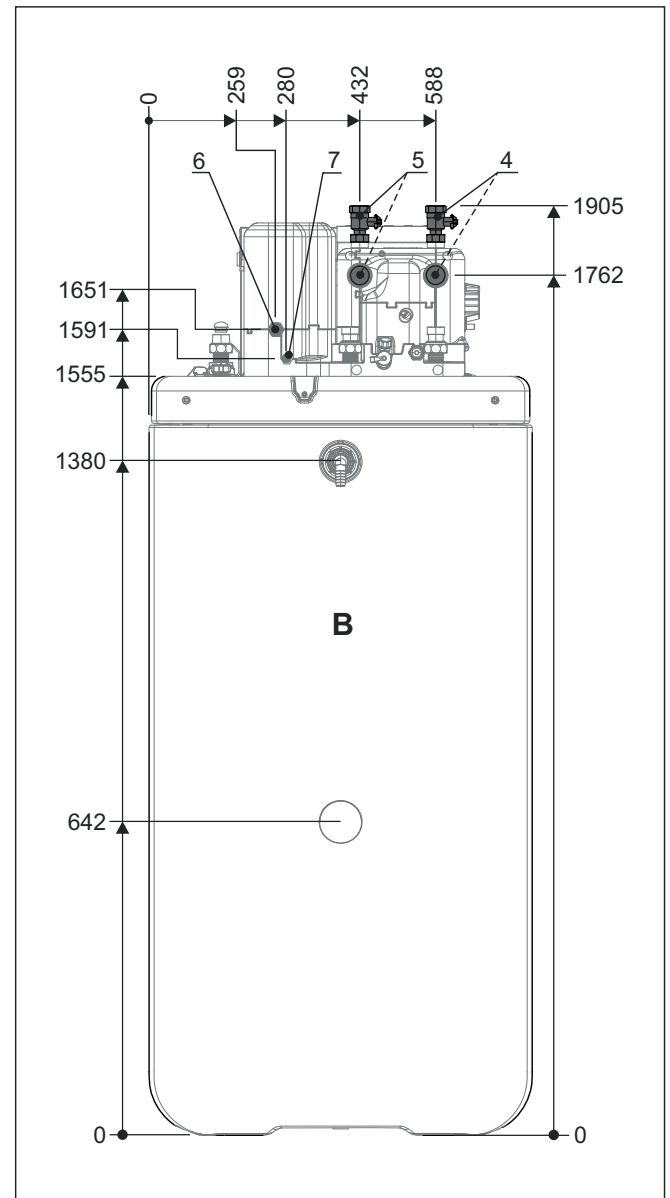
Dimensions vue latérale - Type ...04P50D / ...08P50D
